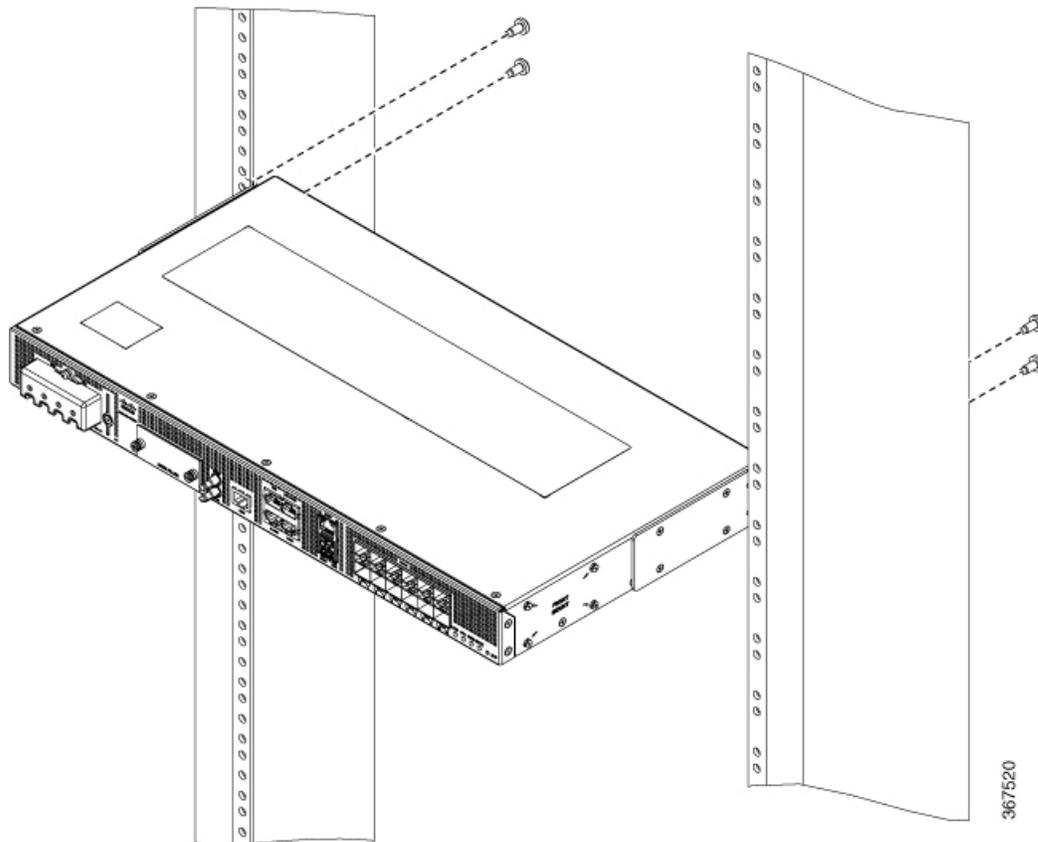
Installer l'appareil sur un rack de 21 pouces (montage avant)
